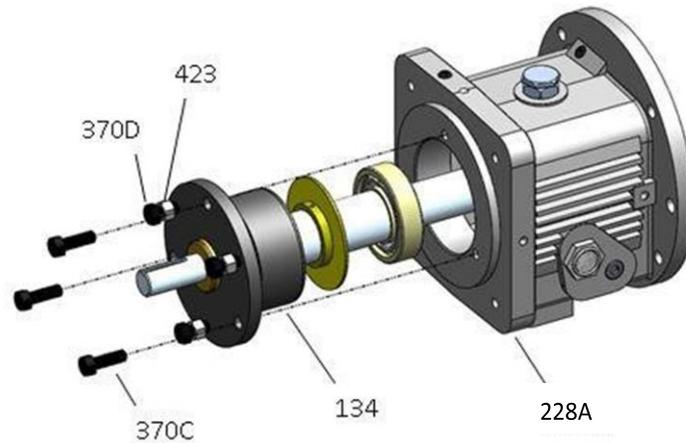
Instalación del montaje de la flecha - rodamiento doble
